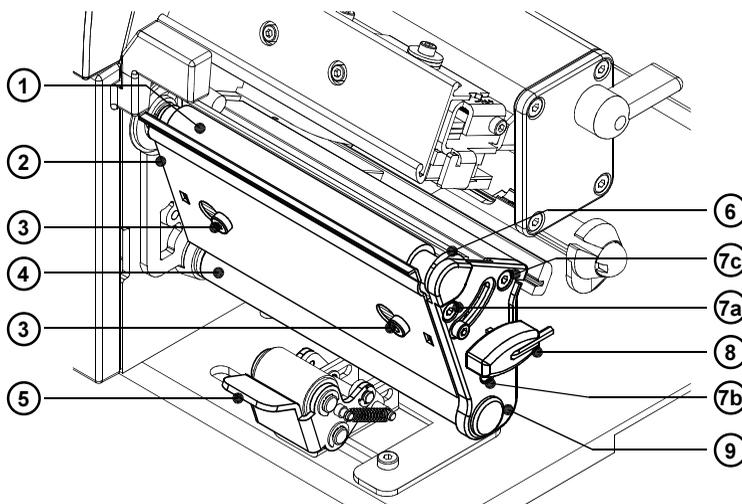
Austausch Druckwalze und Umlenkwalze I
